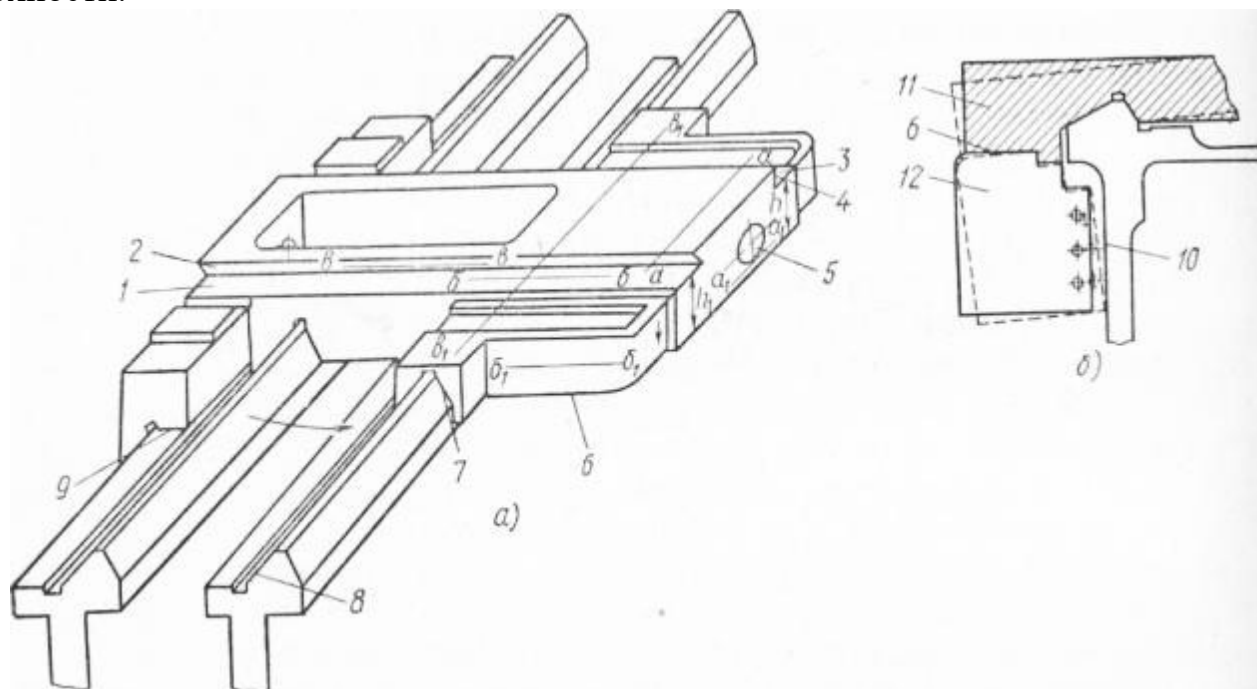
Износ направляющих каретки суппорта токарного станка: а — расположение направляющих, б — наклон каретки и фартука вследствие износа направляющих
